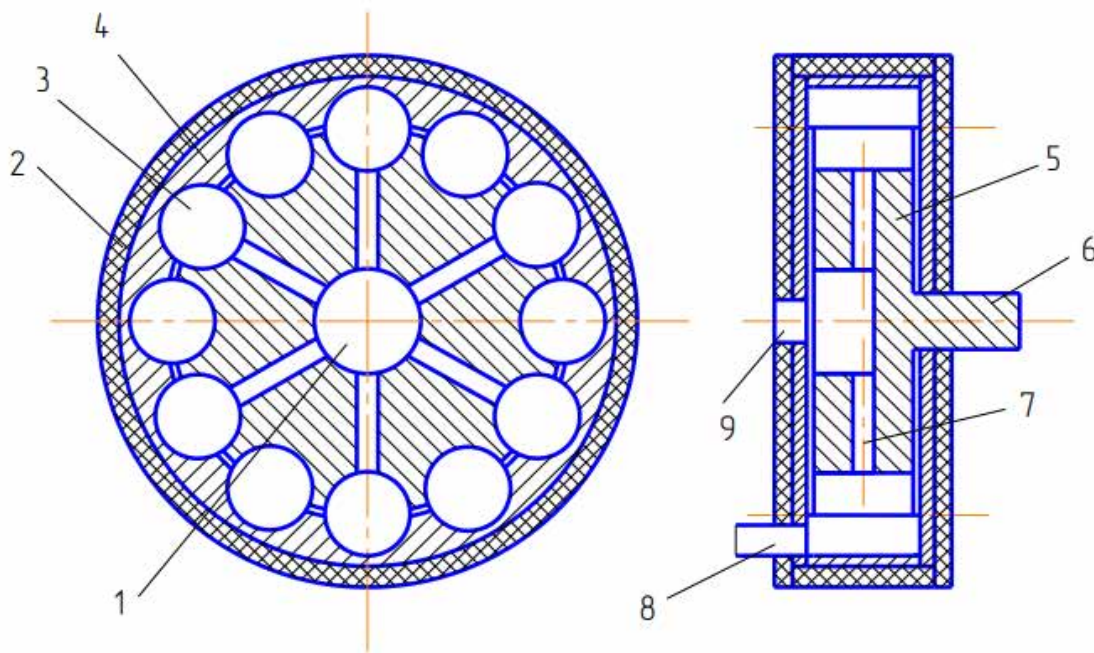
Схема гідродинамічного нагрівача: 1 – розточка ротора; 2 – термоізоляція; 3 - комірка; 4 – корпус; 5 – ротор; 6 – вал; 7 – радіальний канал; 8, 9 – отвори введення та виведення молока
